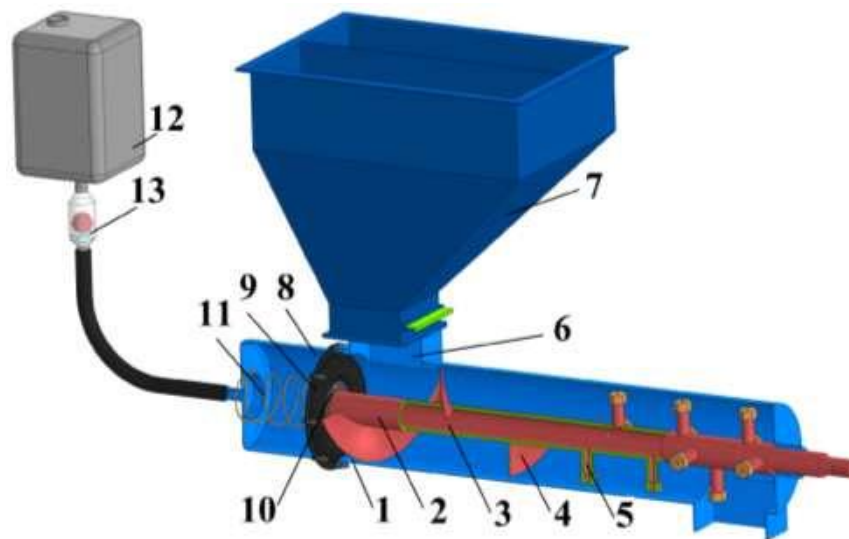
Конструктивна схема змішувача: 1 – корпус; 2 – робочий орган; 3 – вал порожнистий; 4 – конвеєр шнековий; 5 – лопата порожниста; 6 – вхідна горловина; 7 – бункер; 8 – камера ЗКЕ; 9 – мембрана; 10 – опора; 11 – пружина; 12 – ємність накопичувальна ЗКЕ; 13 – клапан зворотний.
